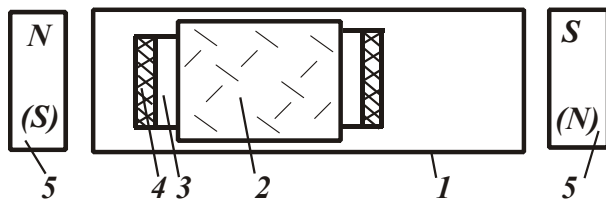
Схема магнито-импульсной обработки цилиндров: 1 – обрабатываемый цилиндр; 2 – шлифовальный круг; 3 – металлический намагничивающийся сердечник; 4 – амортизаторы; 5 – электромагниты.
